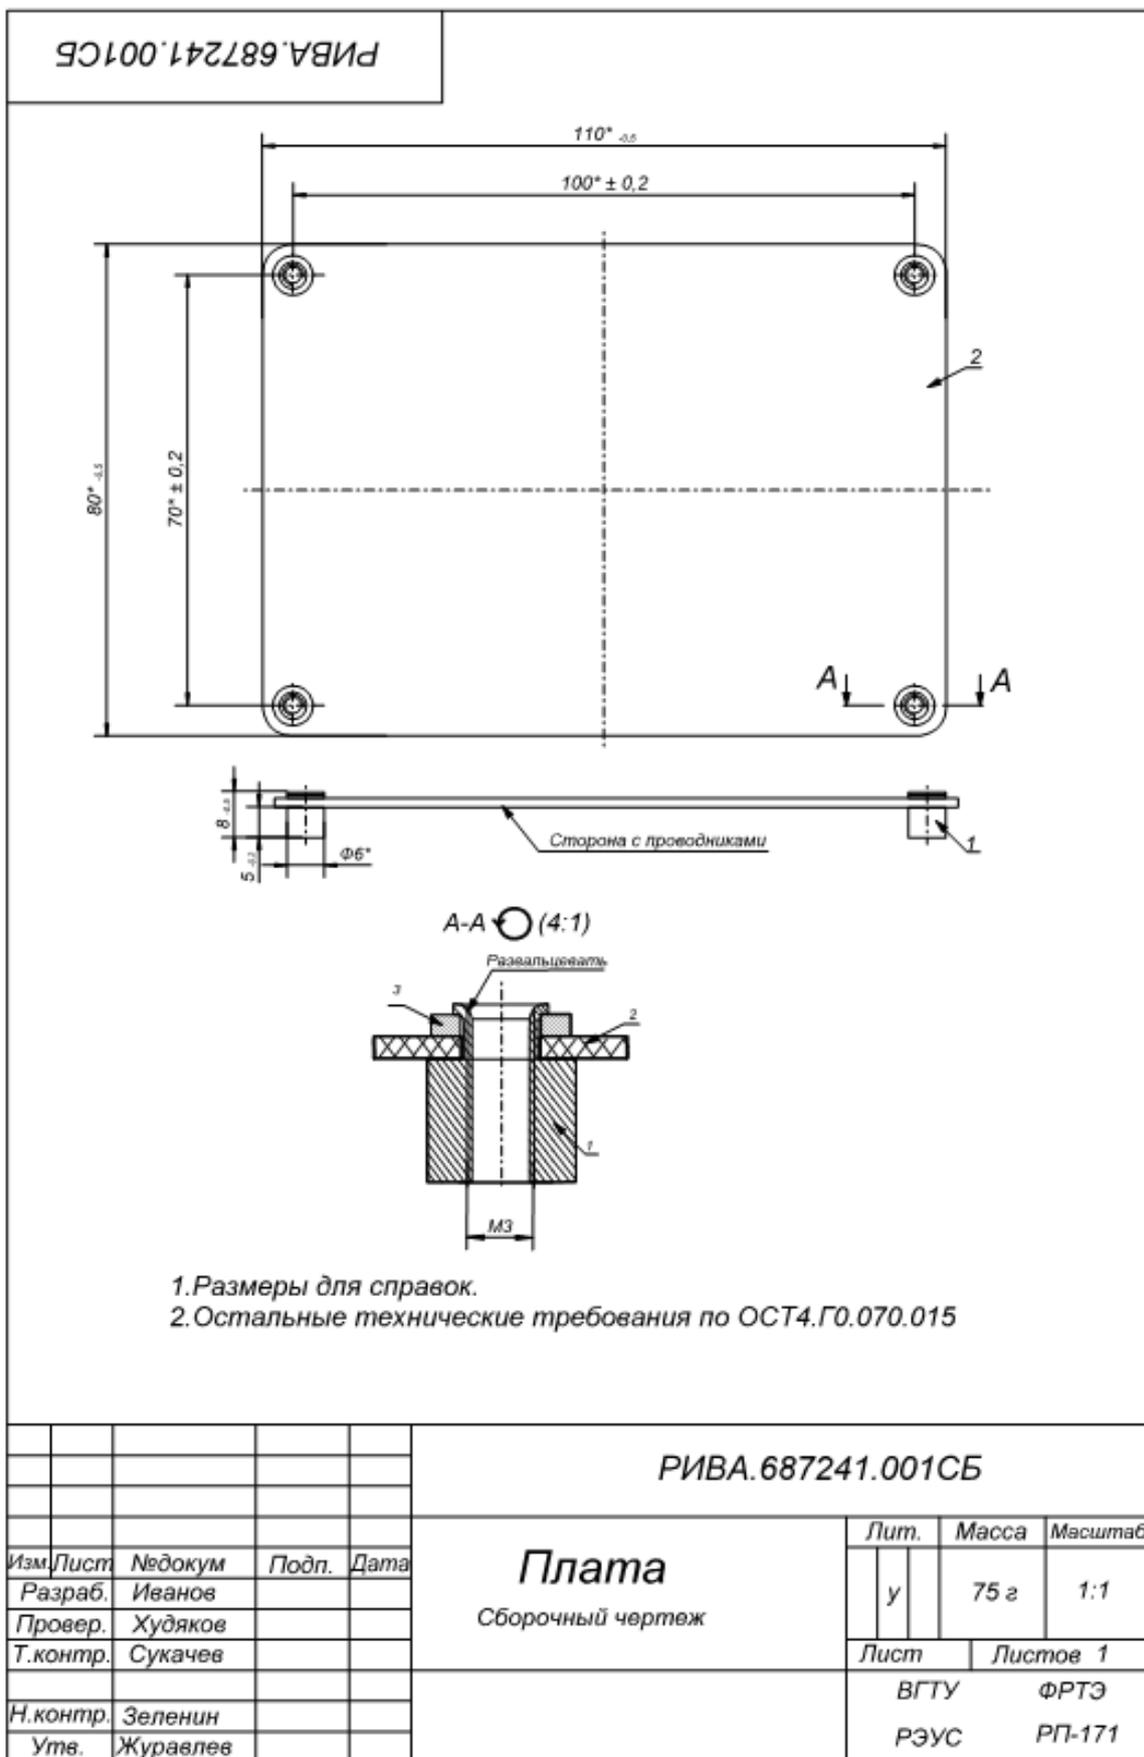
Снимок с экрана сборочного чертежа после установки на печатной плате резбовых втулок
